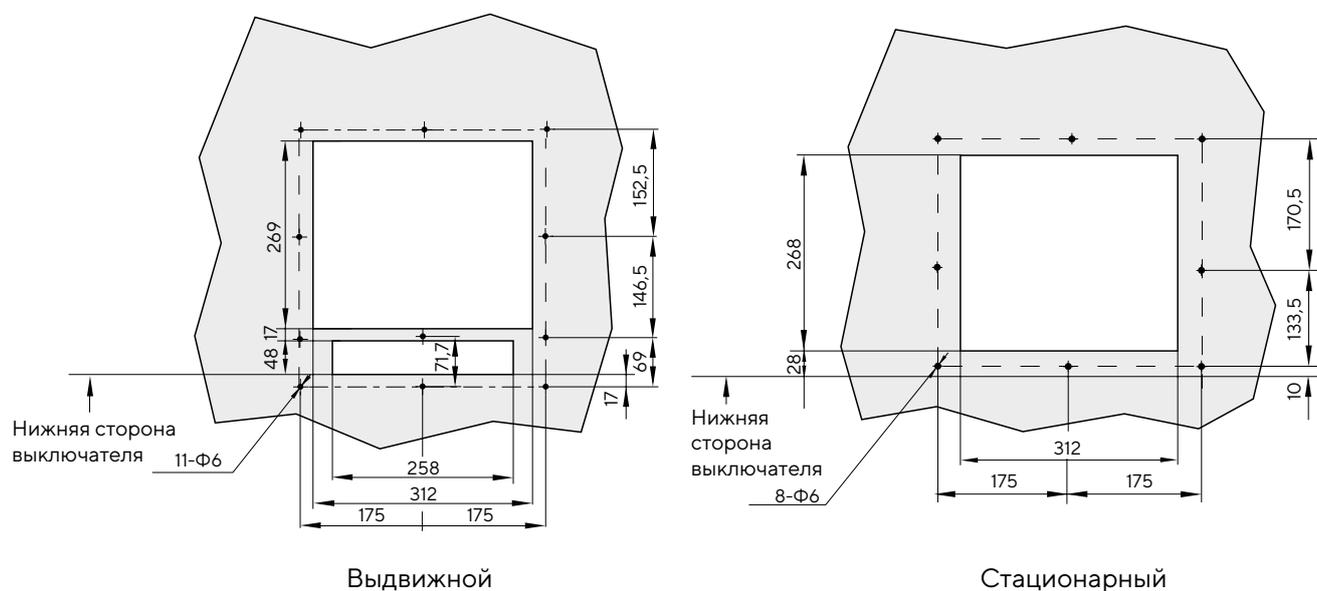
Габаритные размеры рамки обрамления выреза в двери для выключателей типоразмера D
